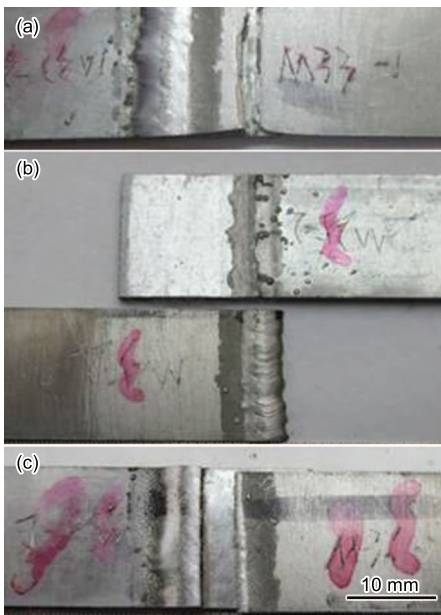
P-MIG 电弧熔 - 钎焊接头断裂位置
